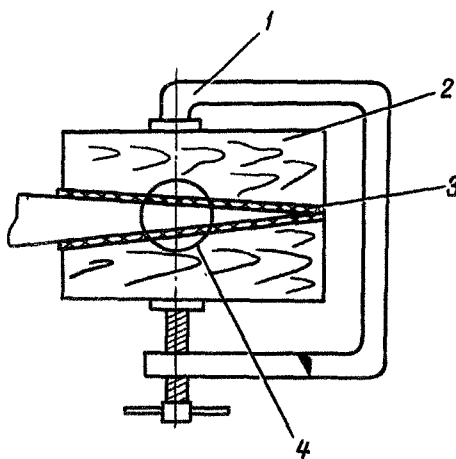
Установка струбины для создания давления в местах склейки обшивки:
